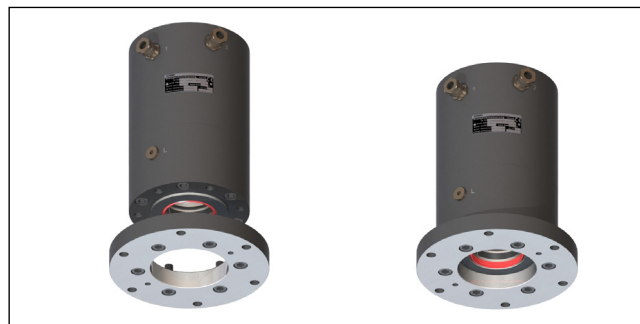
Befestigungsflansch für Stangenblockierungen mit Lastrichtung Druck (Bauart KRG)
